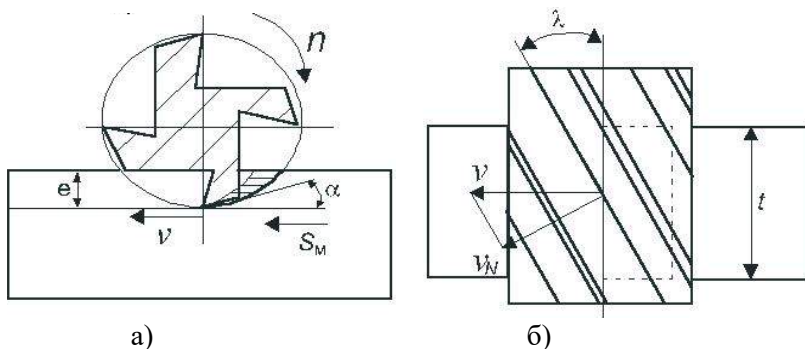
Схема фрезерования цилиндрической фрезой с винтовым зубом
